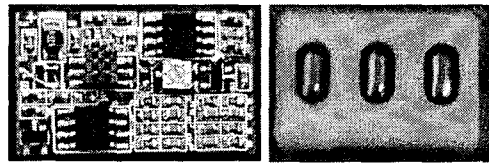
제작된 회로부 PCB 와 조립된 근전위 센서
